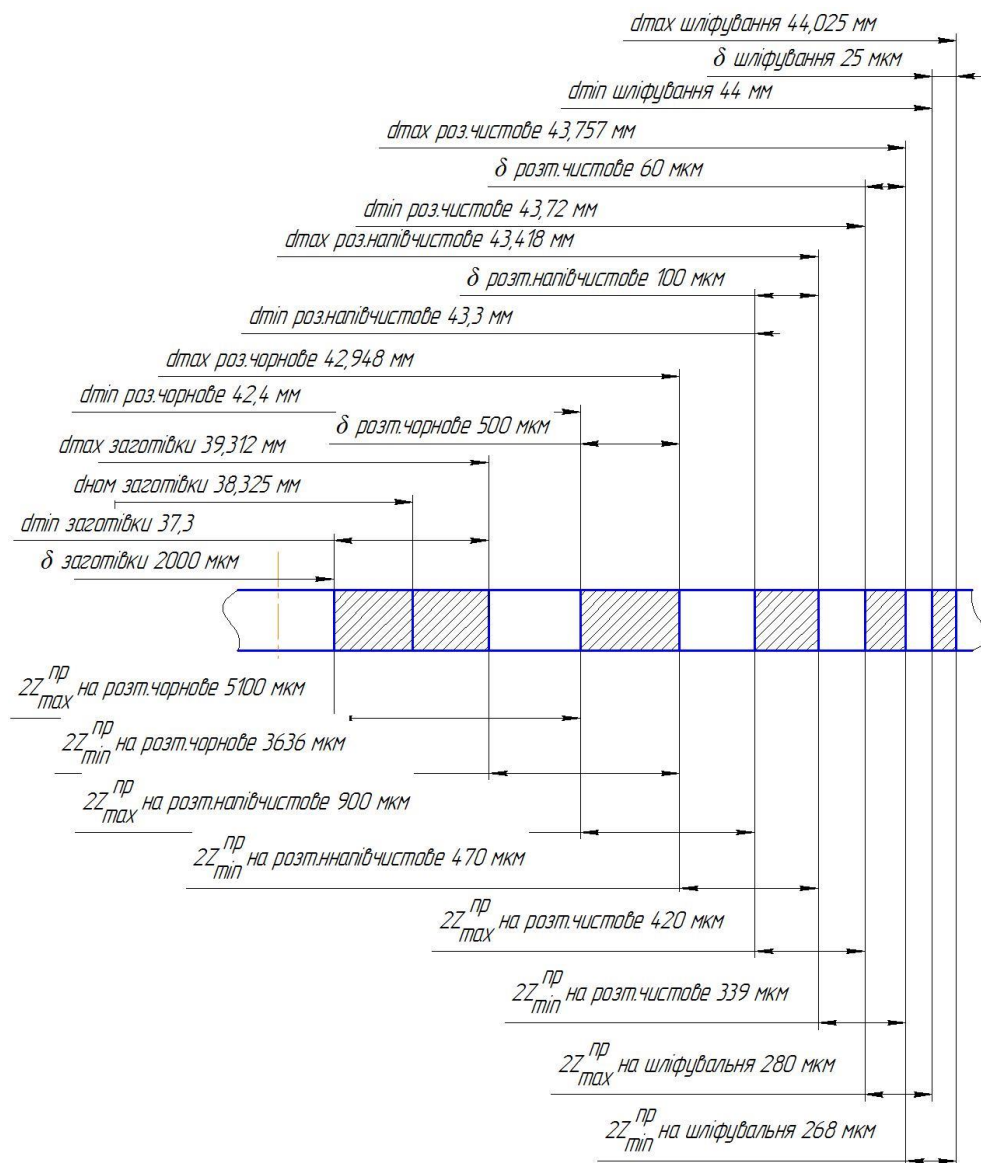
Схема графічного розташування припусків і допусків на обробку
